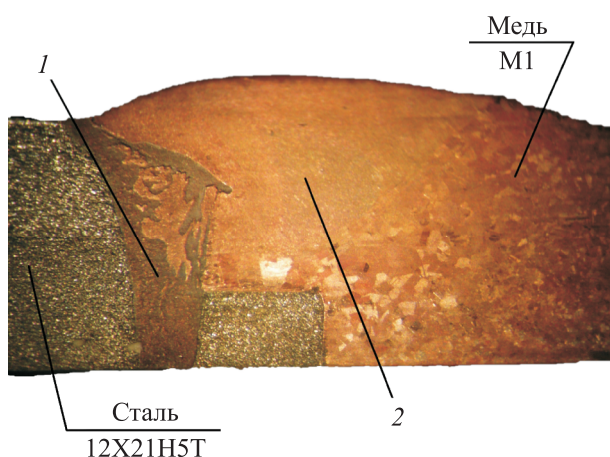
Структура микрошлифа сварного соединения:
